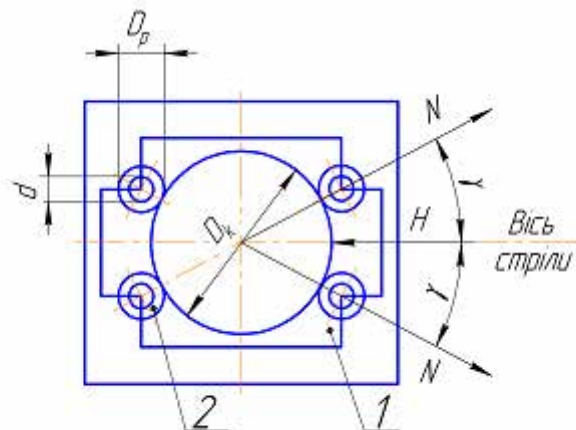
Схема нижнього опорно-поворотного вузла
